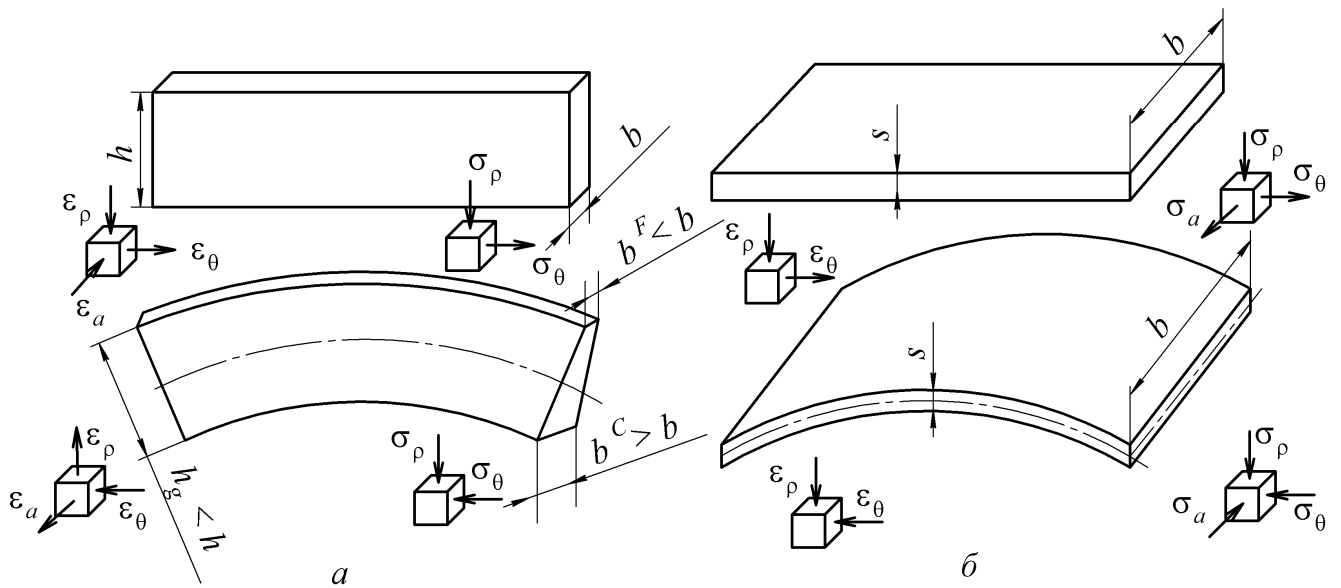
Схема згинання вузької (а) і широкої (б) смуг металу
